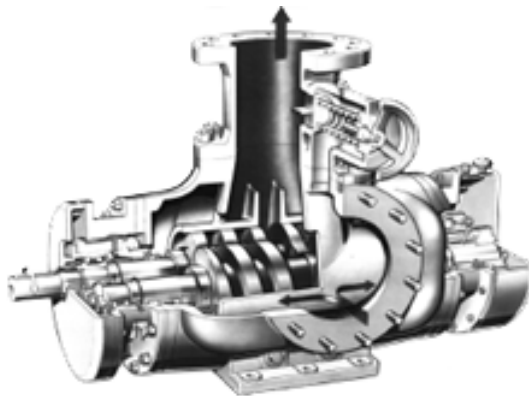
c.- Bomba de tornillo doble; vista de conjunto
